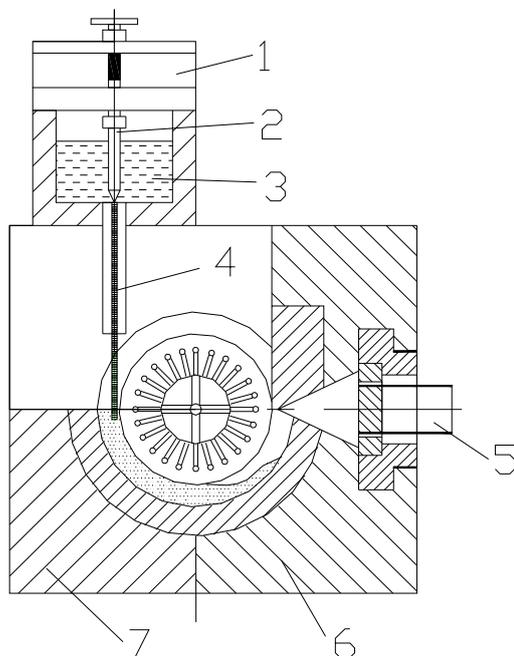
Схема реализации процесса непрерывного литья – прессования способом Conform-Castex: 1 – заливочный ковш; 2 – регулятор уровня; 3 – жидкий металл; 4 – напорная трубка; 5 – пресс-изделие; 6 – прессовый башмак; 7 – башмак для затвердевания
